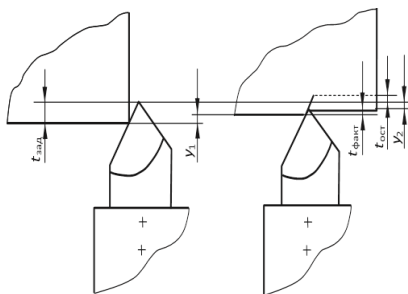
Схема взаимного перемещения инструмента и заготовки при обработке: а — до начала обработки; б — в процессе обработки
